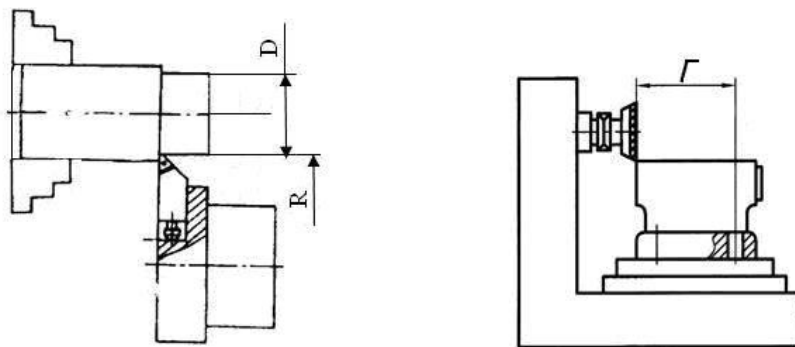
Размеры заготовок, получаемые от обработанных поверхностей
